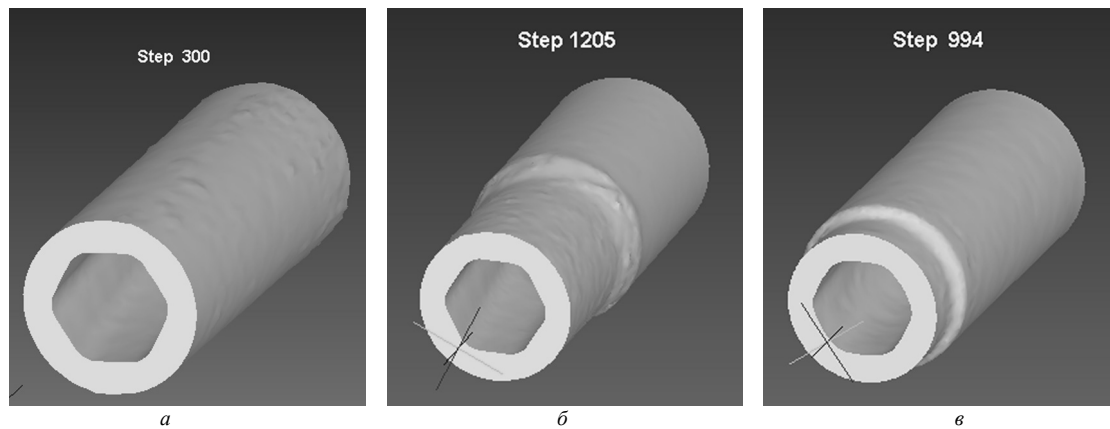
Результат моделювання процесу волочіння: а – через матрицю з циліндричною робочою кромкою; б – через матрицю з гвинтовою двоохвальною робочою кромкою зі спеціальним профілем з кутом робочої конічної частини $\alpha = 15^\circ$; в – через матрицю з гвинтовою двоохвальною робочою кромкою зі спеціальним профілем з кутом робочої конічної частини $\alpha = 45^\circ$
